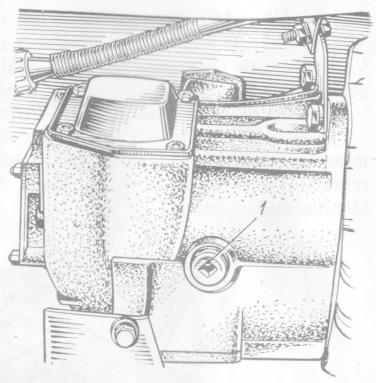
Lage von Einfüllöffnung und Bild 60. Lage der Ablaßschraube des Getriebekastens: 1 — Ablaßschraube
